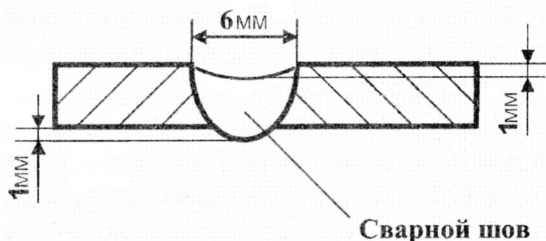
Вид сварного соединения дуговой сваркой в защитном газе неплавящимся электродом
